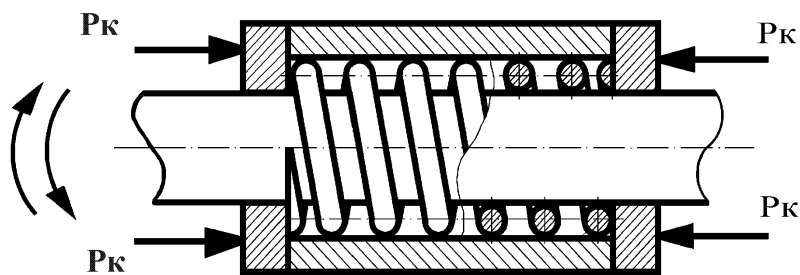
Схема подшипника с подвижным пружинным вкладышем
